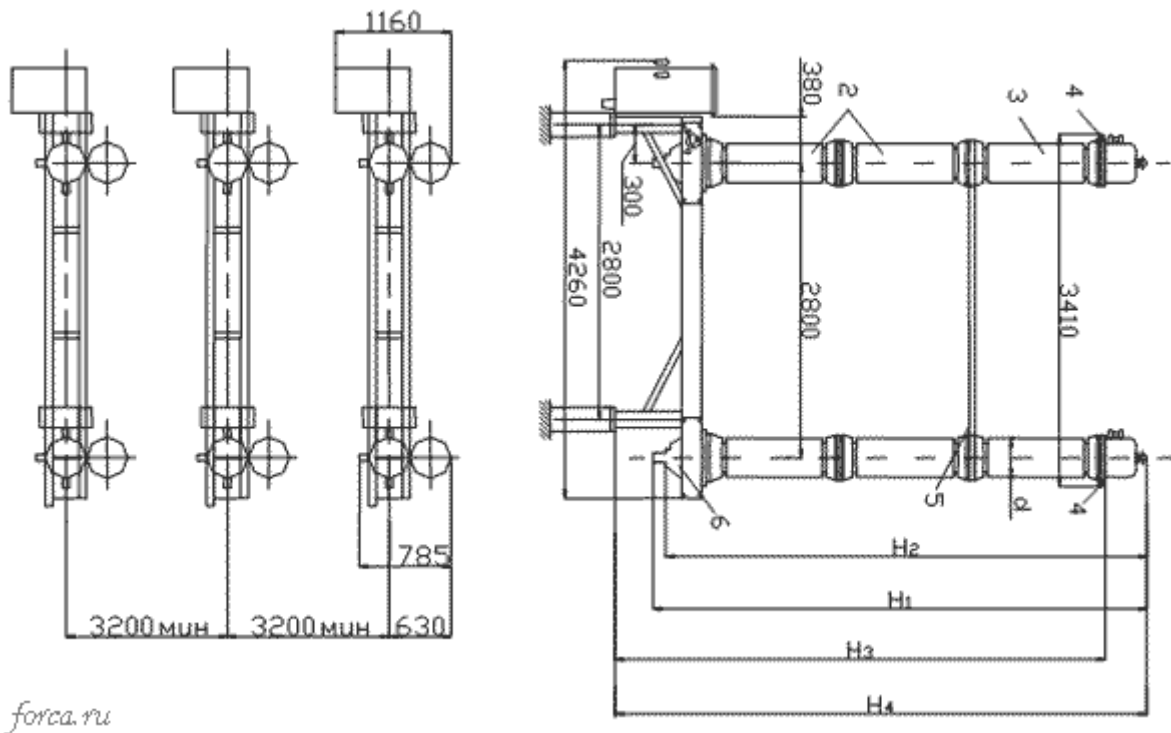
Габаритные, установочные и присоединительные размеры выключателя типа ВМТ-110Б
